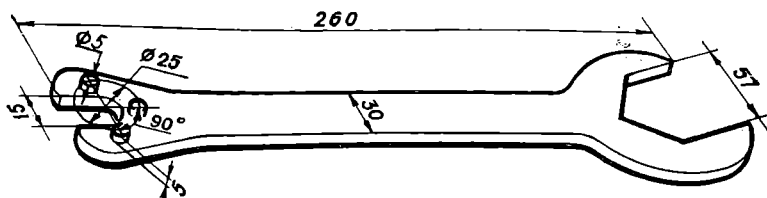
Специальный ключ для разборки амортизатора и стопорной гайки пробки подшипников червяка рулевого механизма.
